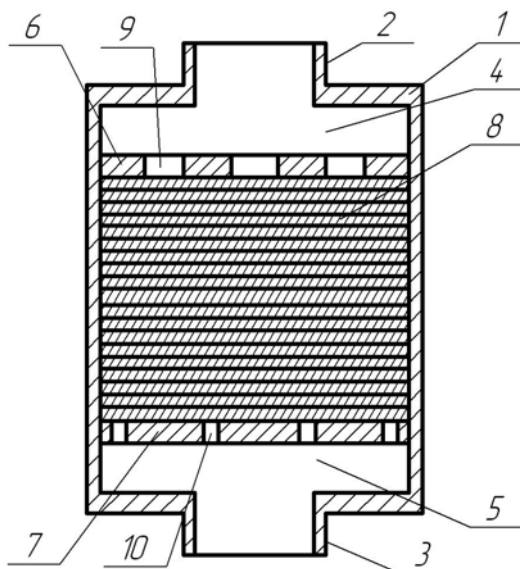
Фильтр для очистки газов, образующихся при сжигании твердых видов топлива: 1 – корпус; 2 – входной патрубок; 3 – выходной патрубок; 4 – подводящая полость; 5 – отводящая полость; 6, 7 – распределительные решетки; 8 – пакет пластин фильтрующего материала; 9, 10 – отверстия в верхней и нижней распределительной решетке
